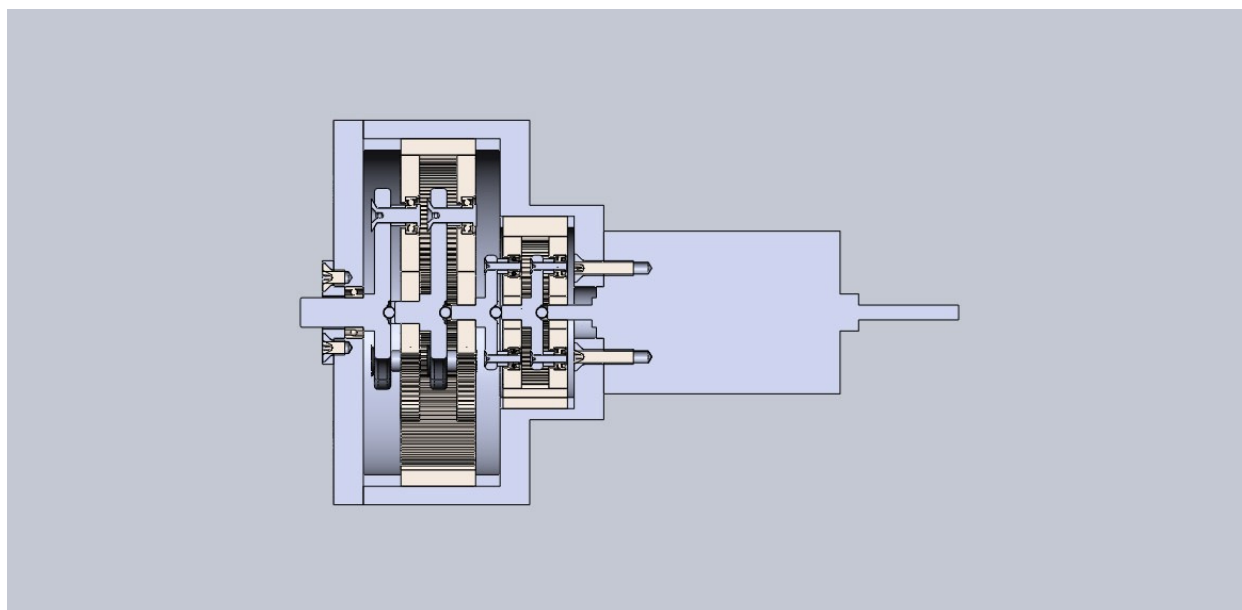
Четырехступенчатый редуктор привода управления гашеткой газа
